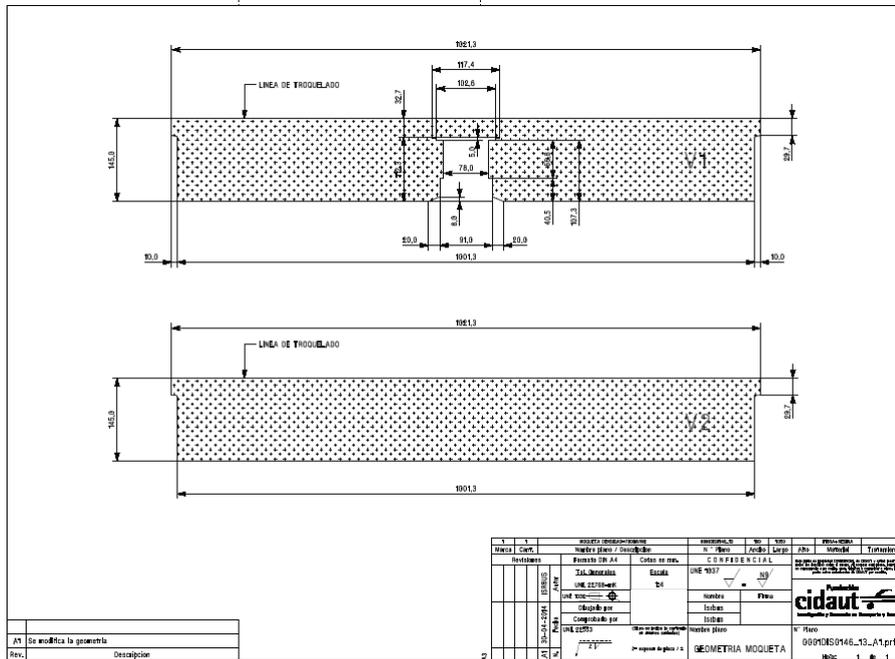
Plano con las dimensiones finales del formato plano de partida para diseño de troquel
